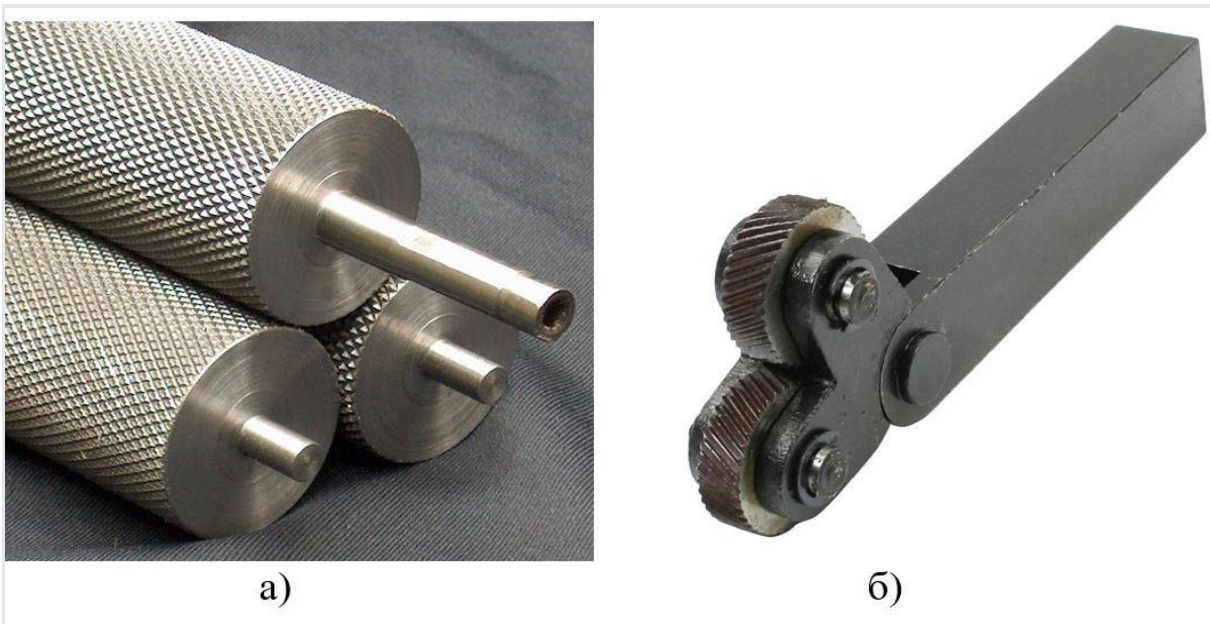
Інструмент для накатки: а) рифлені ролики; б) державка для роликів
